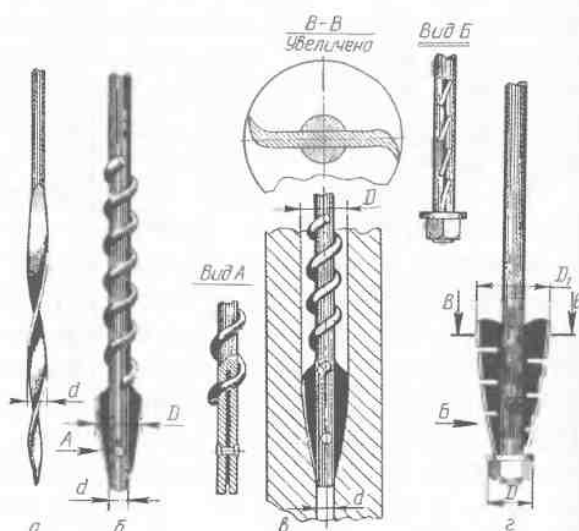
Инструменты для сверления канала вдоль ствола: а — спиральное сверло «жучок» с рабочим диаметром  $d$ ; б — малая коническая перка с направляющим концом диаметра  $d$  и рабочим диаметром  $D$ ; в — положение малой конической перки при сверлении канала; г — большая коническая перка с направляющей шайбой диаметра  $D$  и рабочим диаметром  $D_1$
